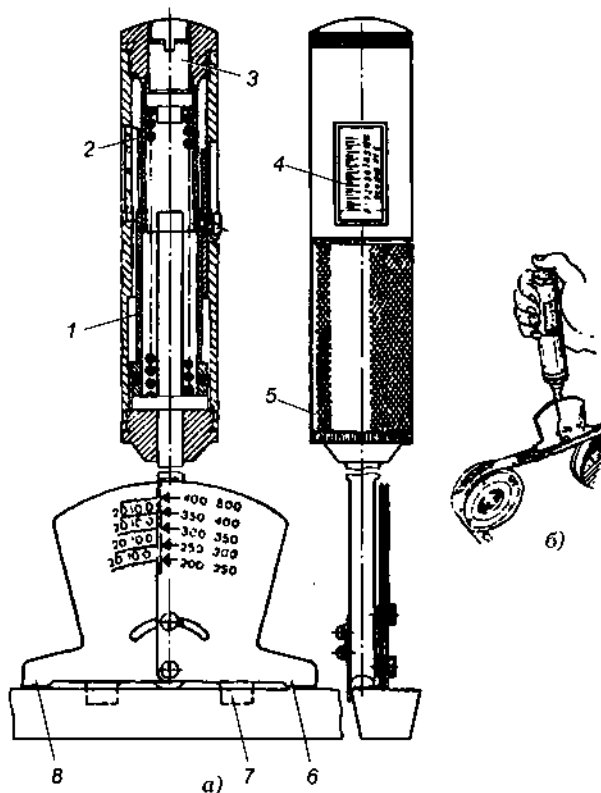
Приспособление КИ-8920 (а) и способ (б) проверки натяжения ремней: 1 — корпус; 2 — пружина; 3 — регулировочный винт; 4 — шкала динамометра; 5 — рукоятка; 6 и 8 — лапки; 7 — фиксаторы
